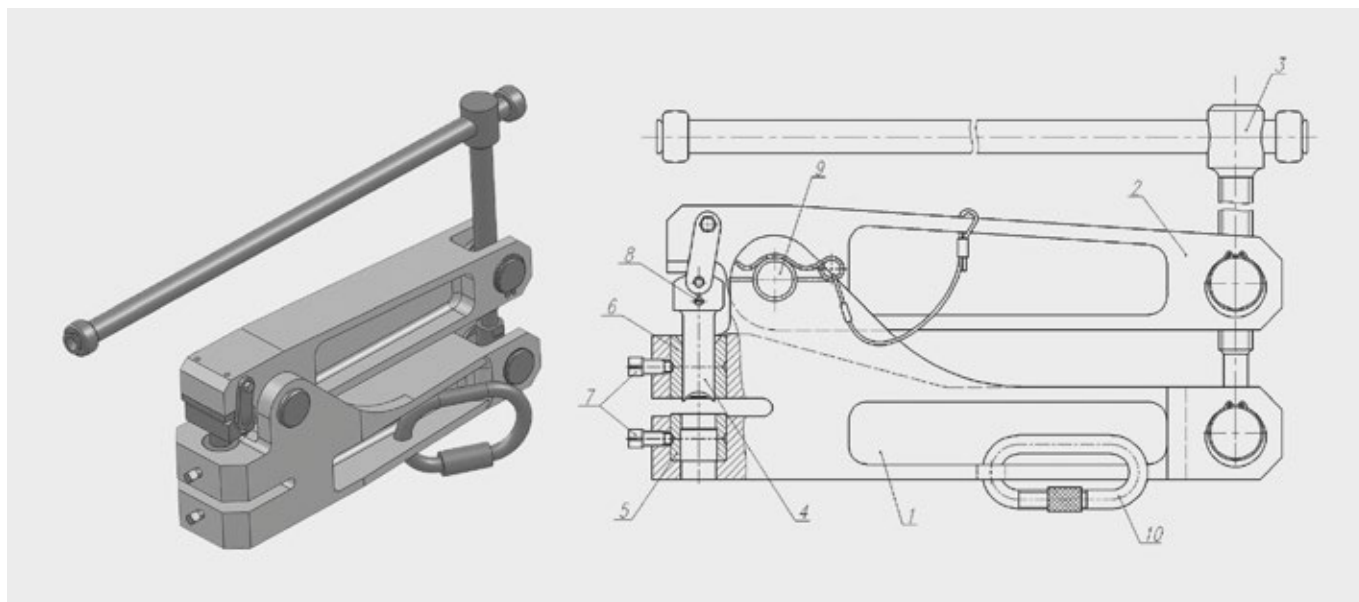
Конструкция пробойника: 1 — корпус; 2 — рычаг; 3 — винтовой механизм; 4 — пуансон; 5 — матрица; 6 — обойма пуансона; 7 — винты стопорные; 8 — винты крепления пуансона; 9 — ось; 10 — карабин такелажный
